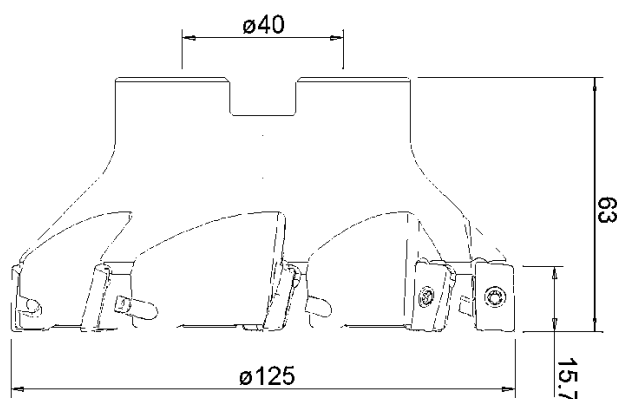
Фреза торцевая CoroMill 390 R390-125Q40-17M
